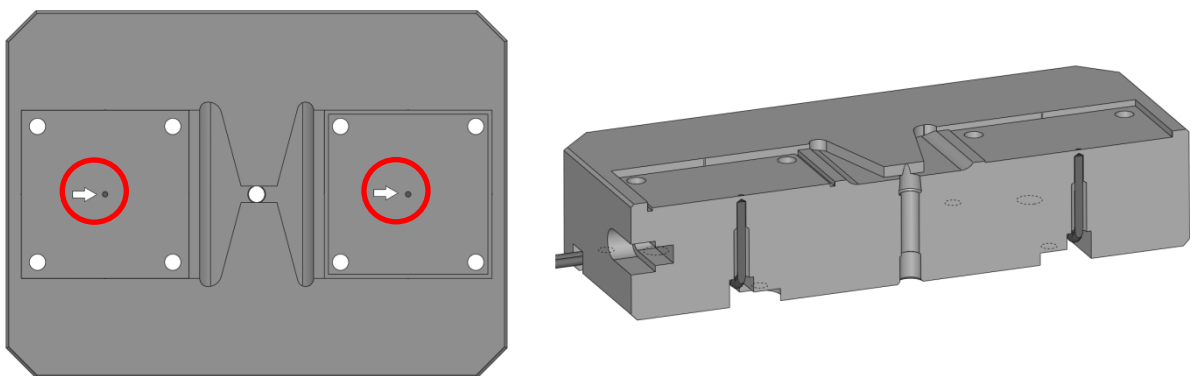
Dimensões do sistema de refrigeração para o inserto macho
